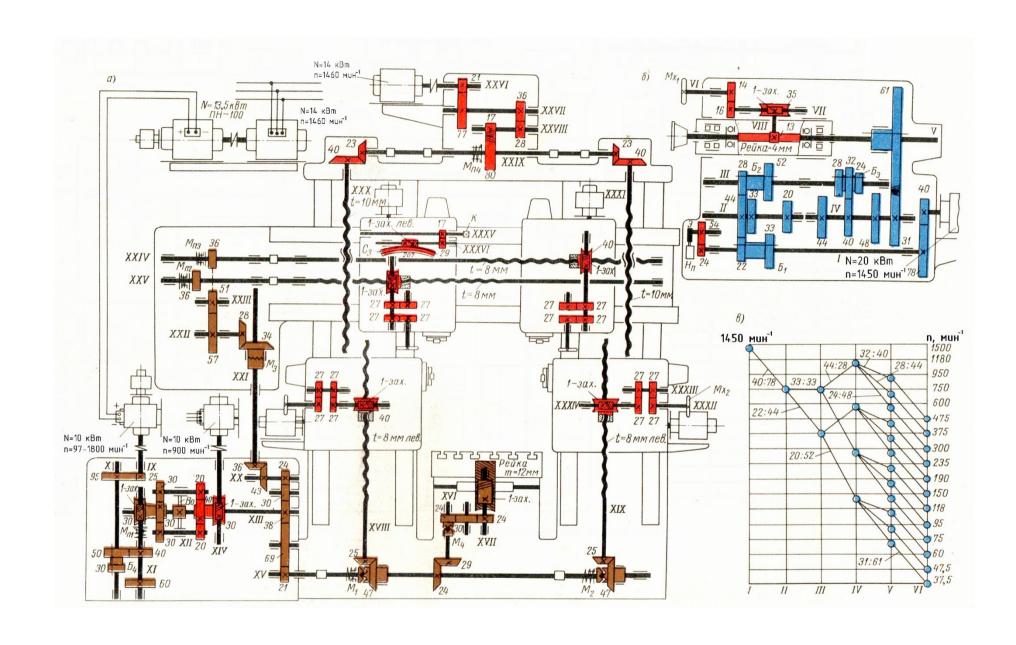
Кинематическая схема продольно-фрезерного станка модели 6652
